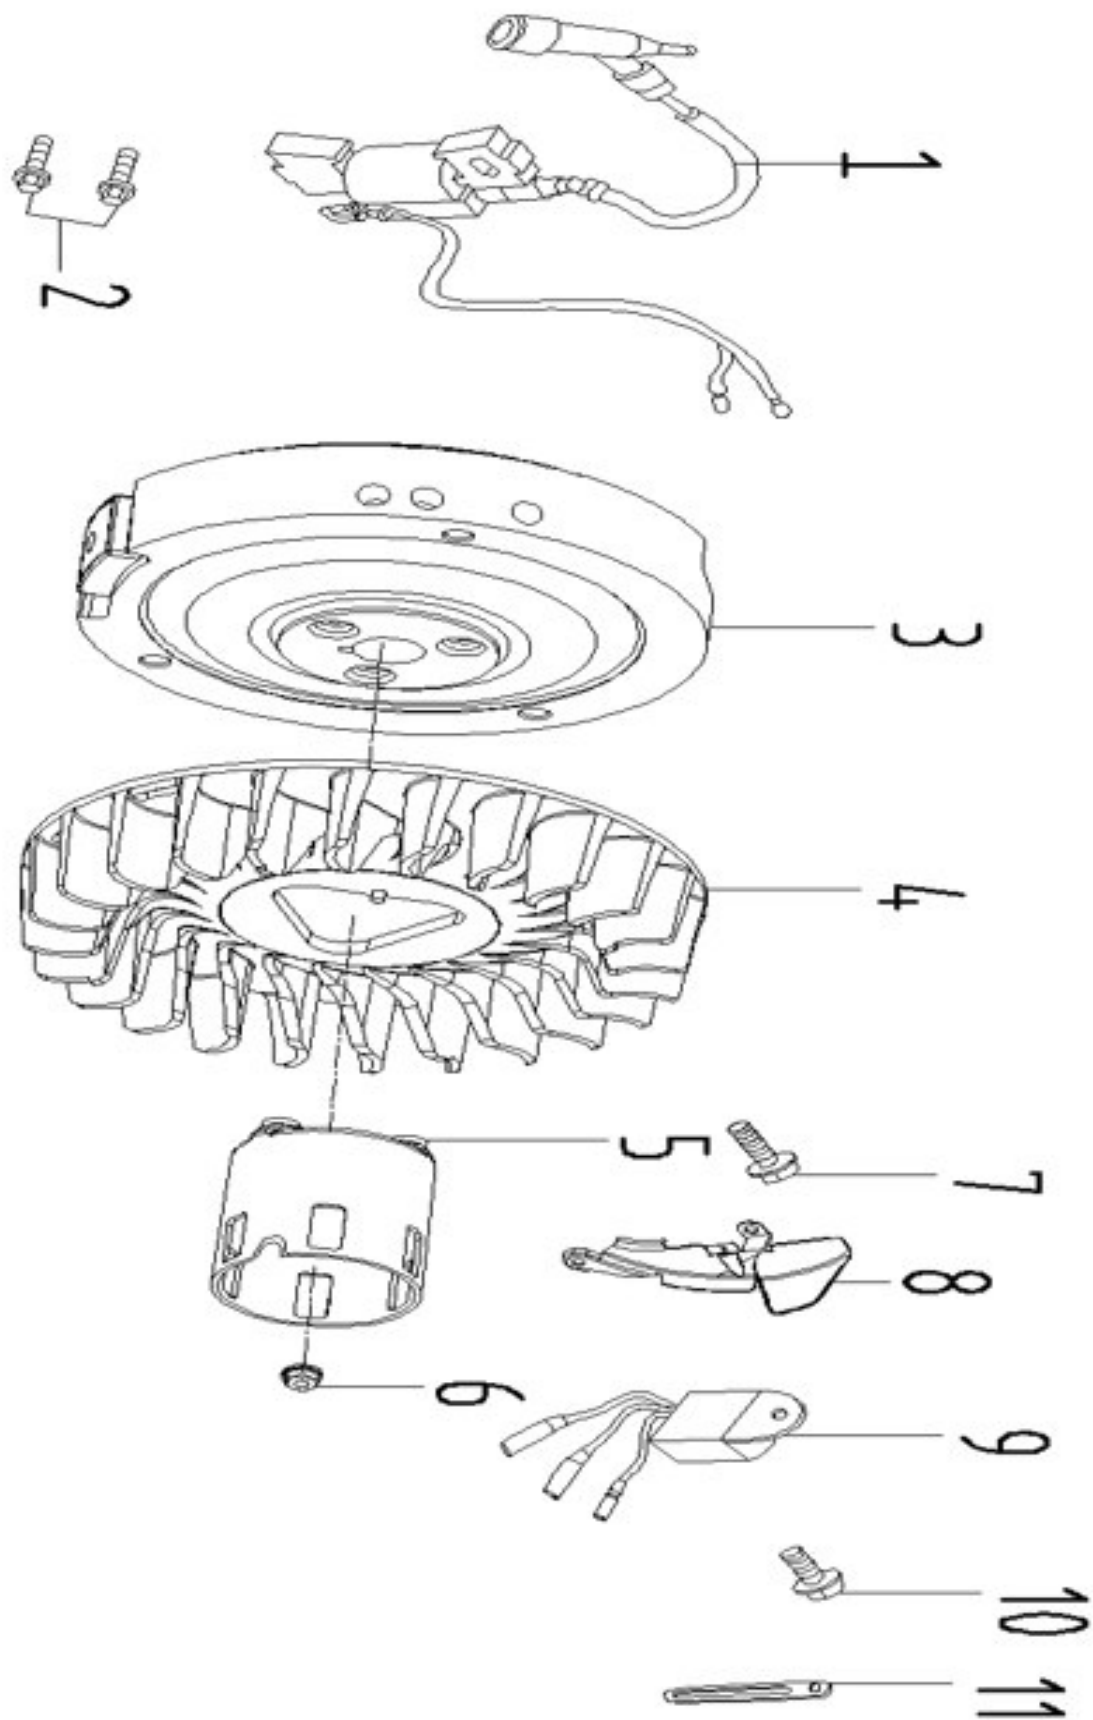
Ersatzteilzeichnung 11 - Schwungrad
